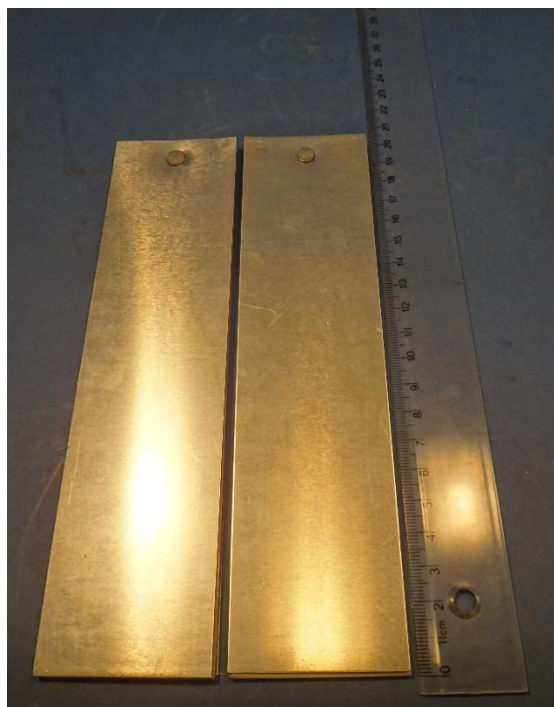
Пакети-заготовки зібрані перед прокаткою за допомогою заклепки
